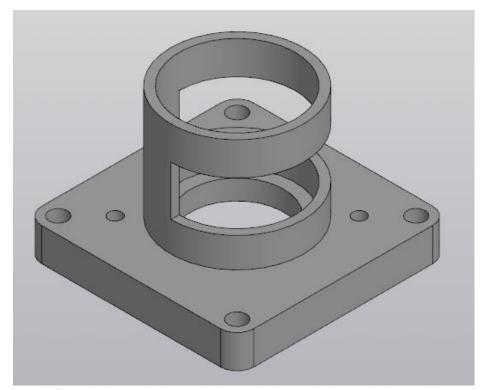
Твердотельная модель детали «Корпус подшипника»
